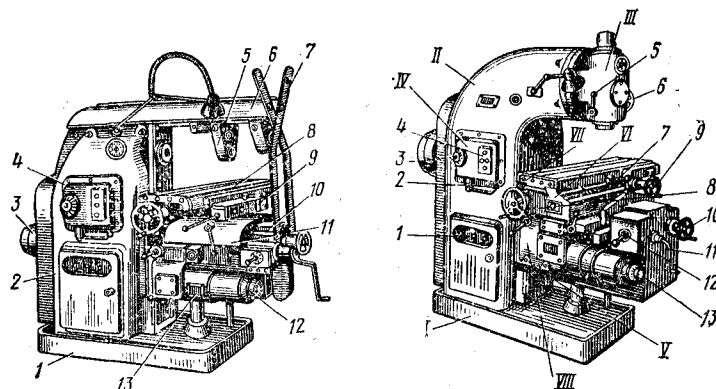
Горизонтально-фрезерный станок модели 6М82
